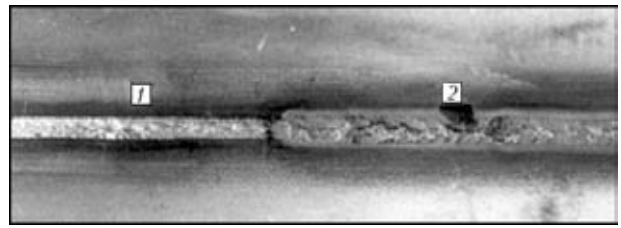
Внешний вид лицевой поверхности сварного соединения до (1) и после (2) обработки
